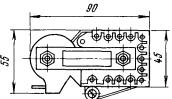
Общий вид трансформаторов строчной развертки типа ТВС-110П3
